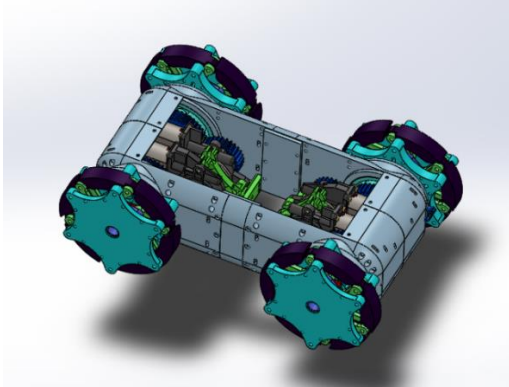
Motor Destek Parçası Solidworks Tasarımı
